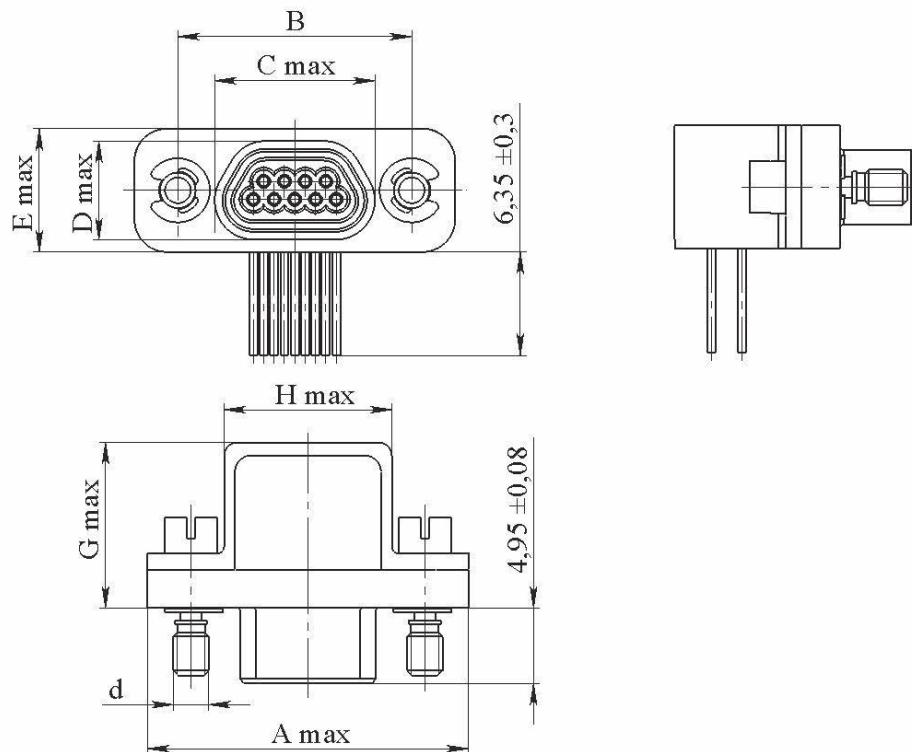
Соединитель СП397-4...Г212В6С2
